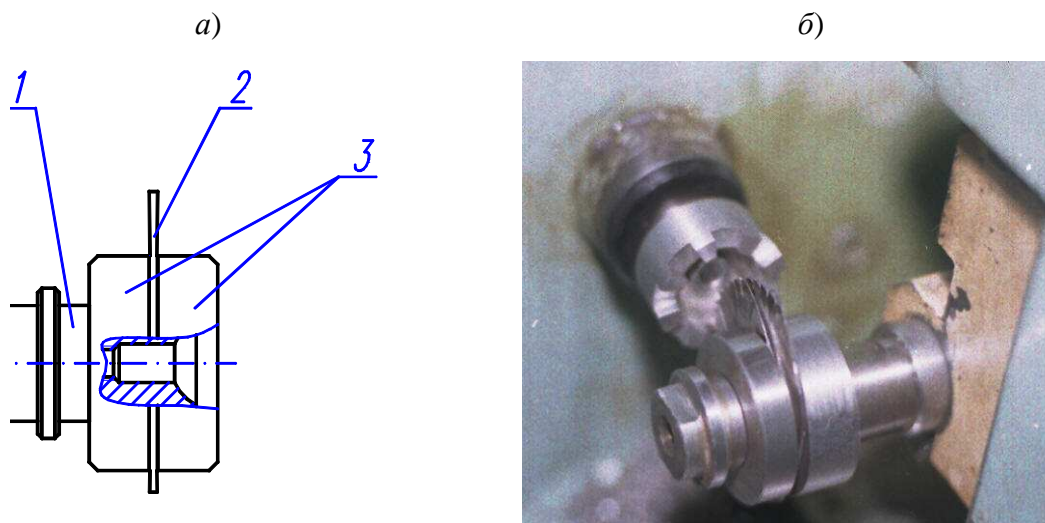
Конструкция секторного инструмента (а) первого типа и пример его применения (б) для обработки широких пазов на зубофрезерном станке модели 5А308П
